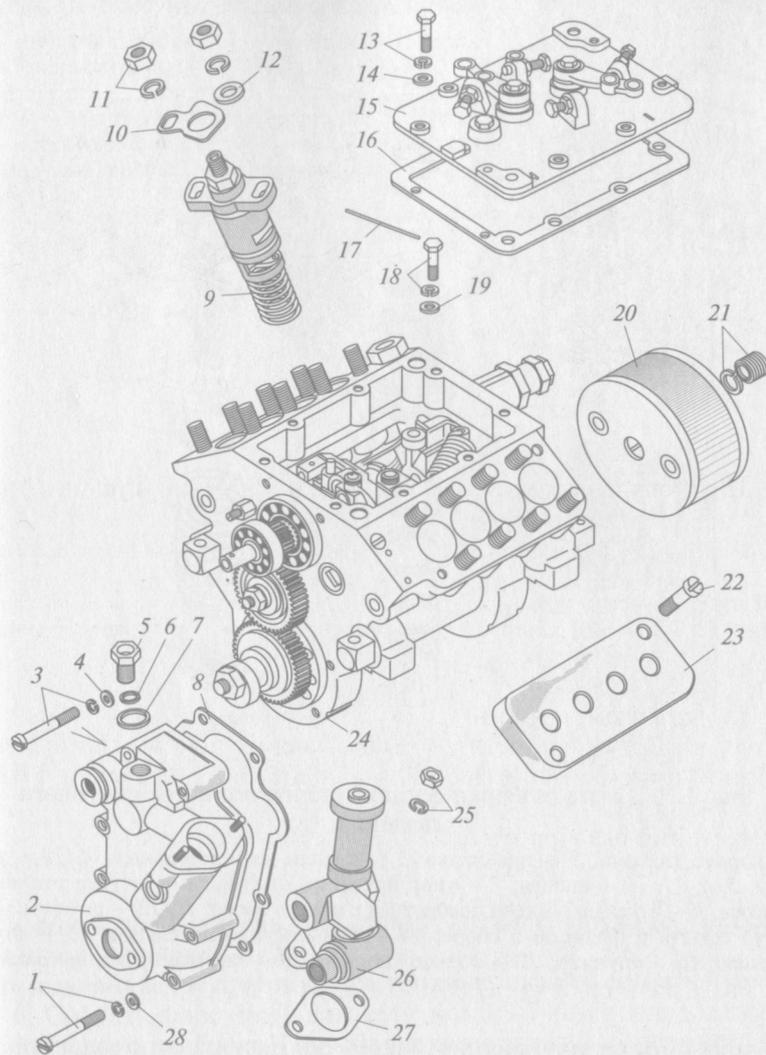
Схема разборки топливного насоса высокого давления:
